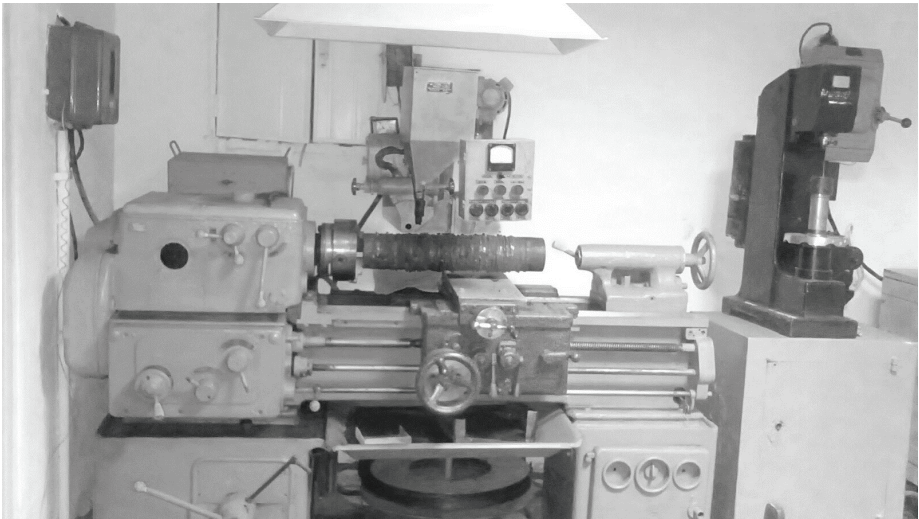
Установка для наплавлення під шаром флюсу А-580М
